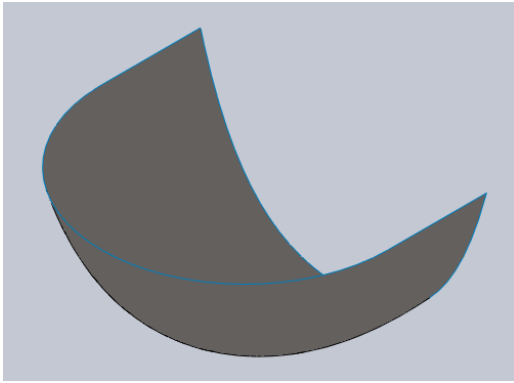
Vista isométrica- Mitad de cuchara. Fuente: Autores.
